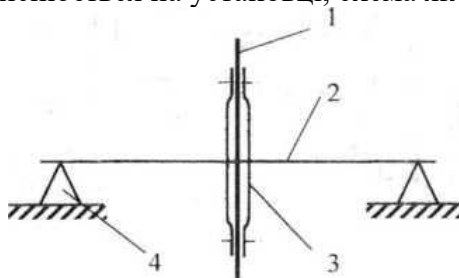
Схема установки для балансування дисків: 1 – диск; 2 – вал; 3 – планшайба; 4 - призма
